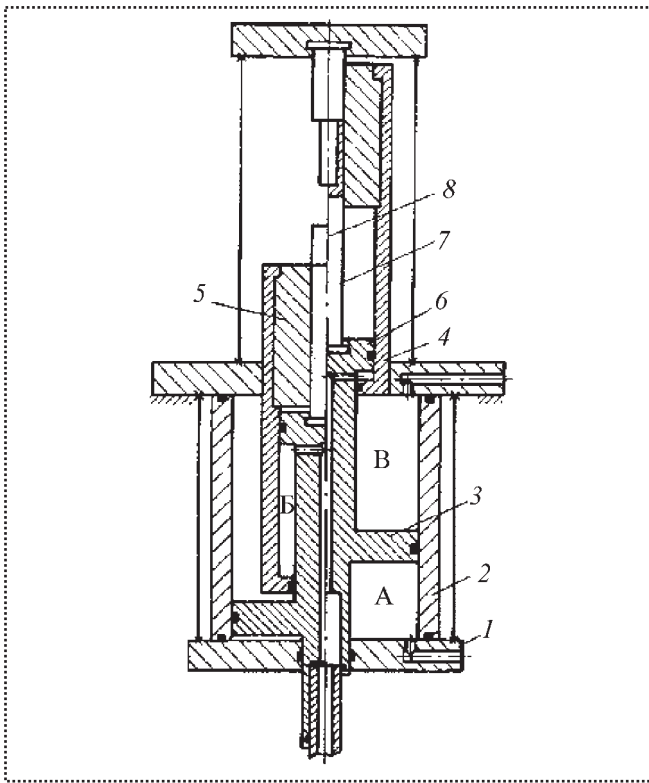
Конструкция особо малогабаритного пресса для выдавливания с активными силами трения
